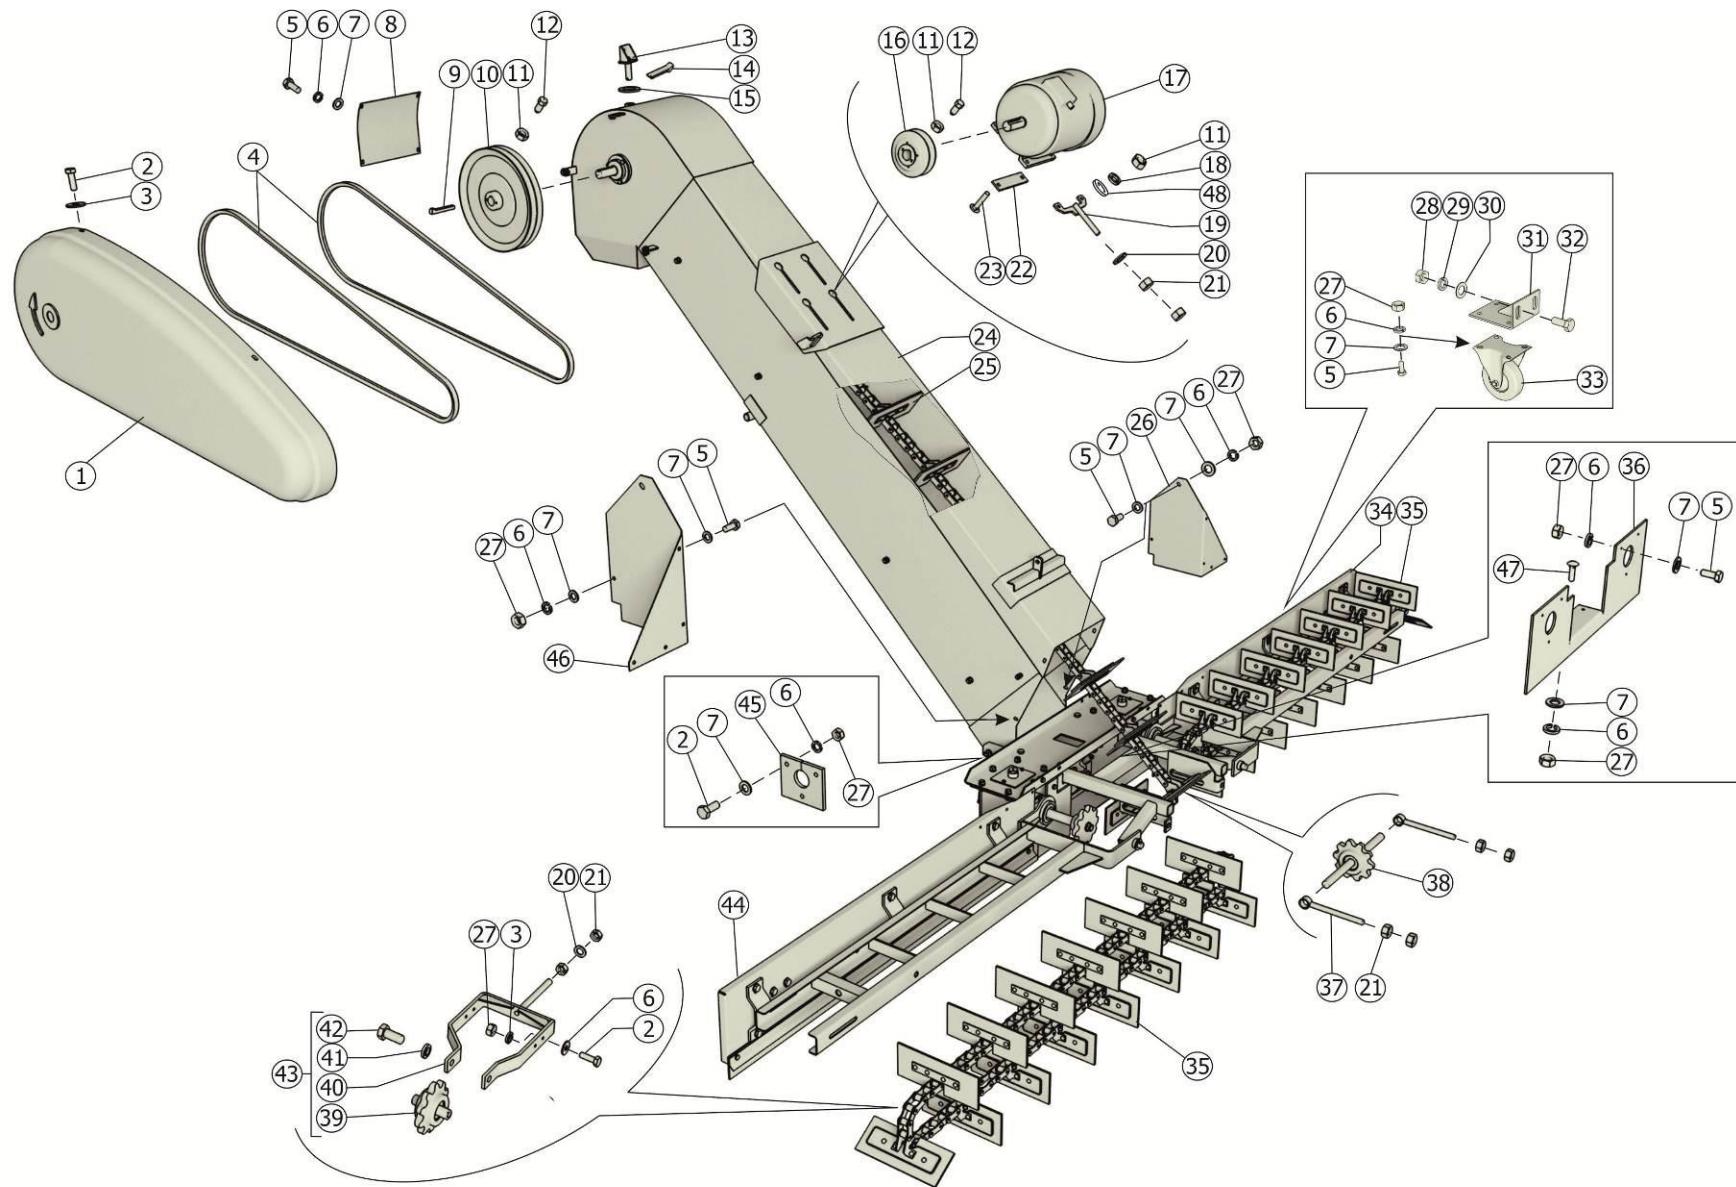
Транспортер загрузочный МЗС-90.03.000
